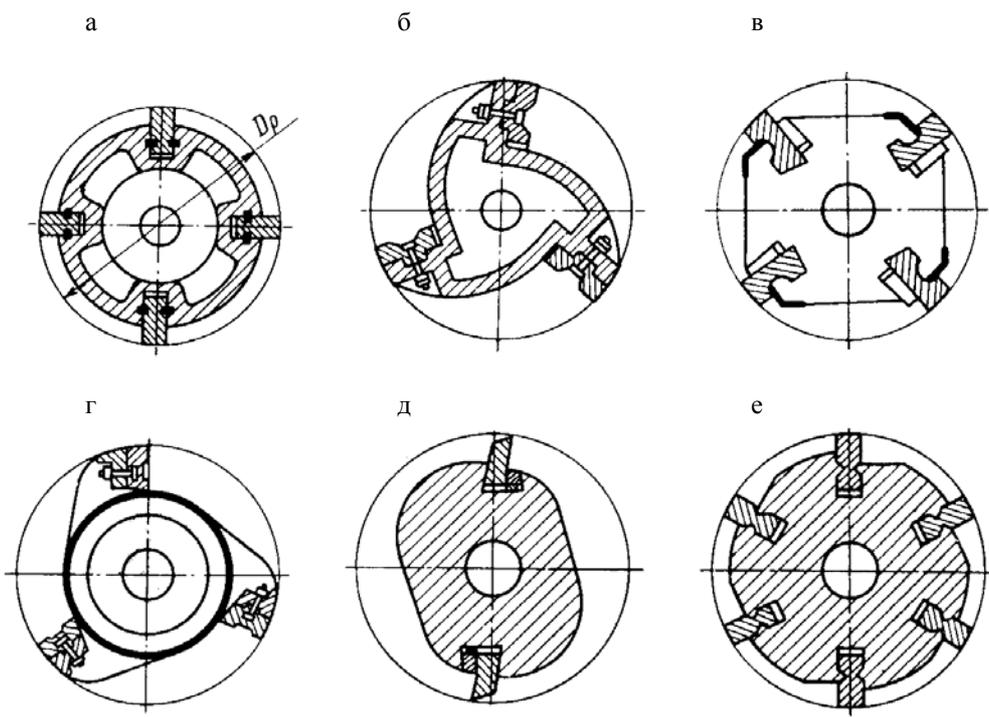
Конструкції корпусів роторів: а – закритий з обрисом зовнішньої поверхні по колу; б – закритий з обрисом зовнішньої поверхні за спіраллю; в – корпус з дисків із зовнішньою поверхнею у вигляді багатокутника; г – закритий з обрисом зовнішньої поверхні по колу з виступами; д – закритий монолітний овальний корпус; е – закритий монолітний циліндричний корпус із зрізаними передбильними частинами
